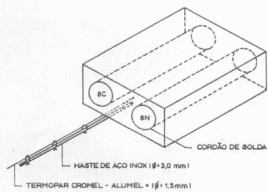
Conjunto placa mãe/amostras cilíndricas, e em detalhes a fixação do termopar.
